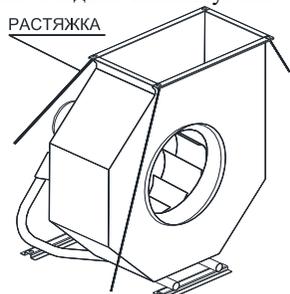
Общий вид вентилятора стандартного исполнения
